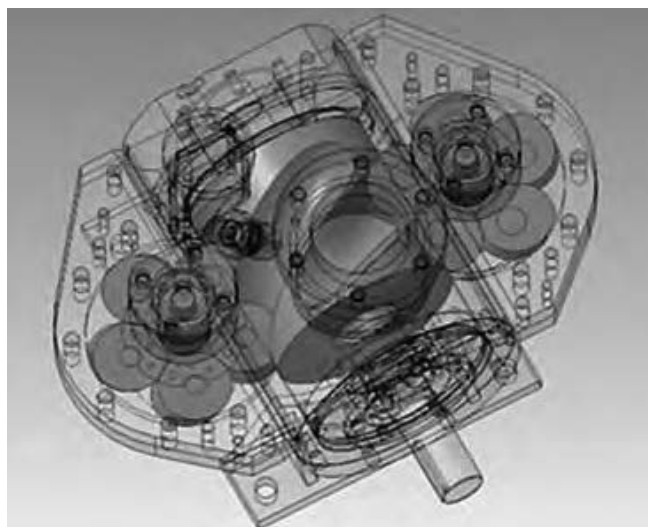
Винтовой однороторный компрессор с окружным профилем зуба отсекаателя (ВКО)
